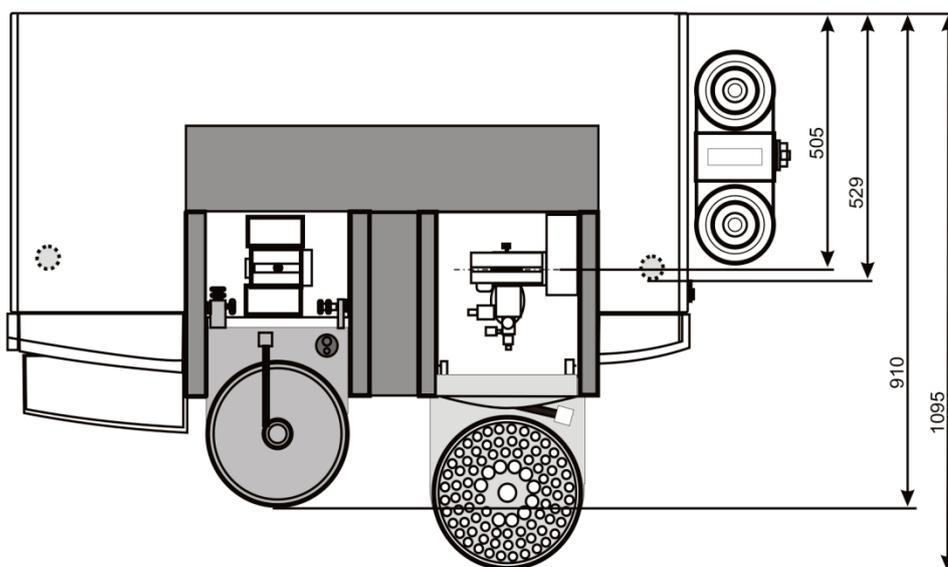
Dimensions ZEEnit 700 P - Vue de dessus
